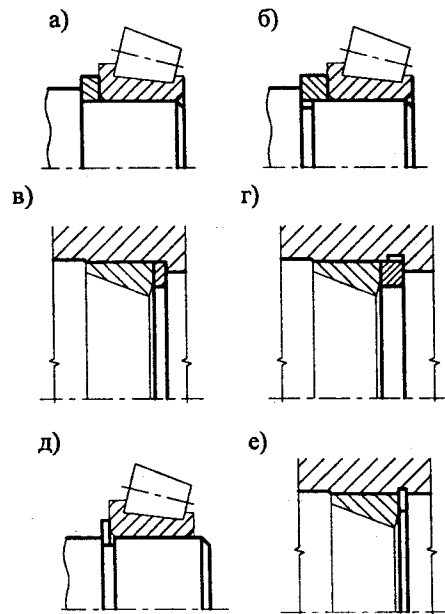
Конструктивные решения по уменьшению высоты заплечиков валов (корпусов) в месте установки подшипника:
